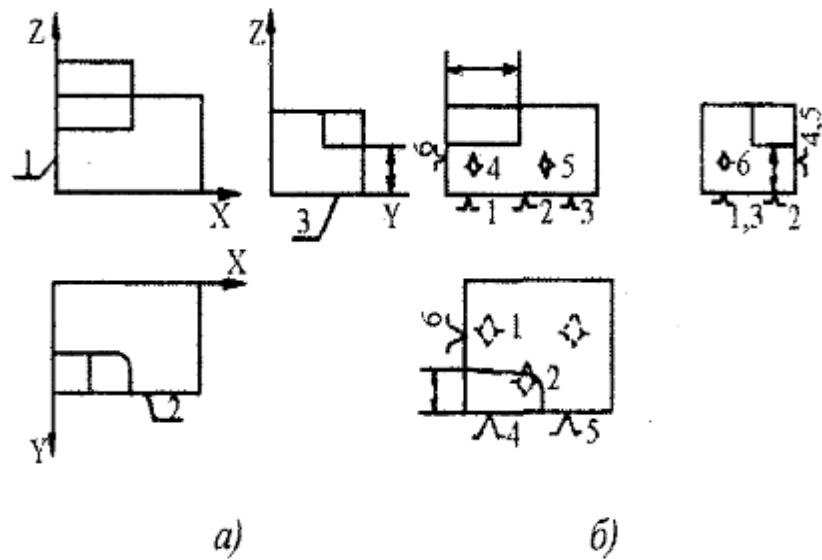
Координація поверхонь уступу (а) і теоретична схема базування заготовки при обробці (б)
